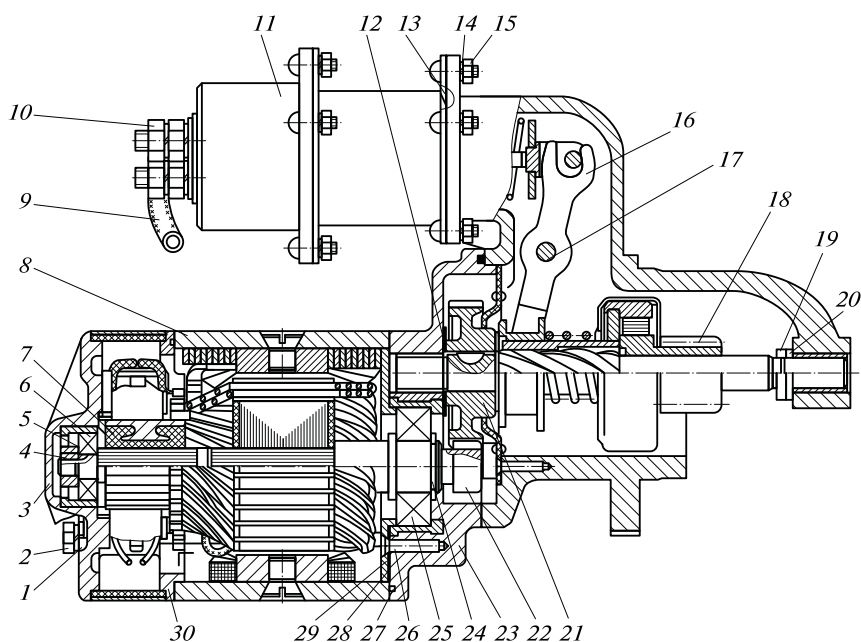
Конструкция стартера со встроенным цилиндрическим редуктором с внешним зацеплением:
